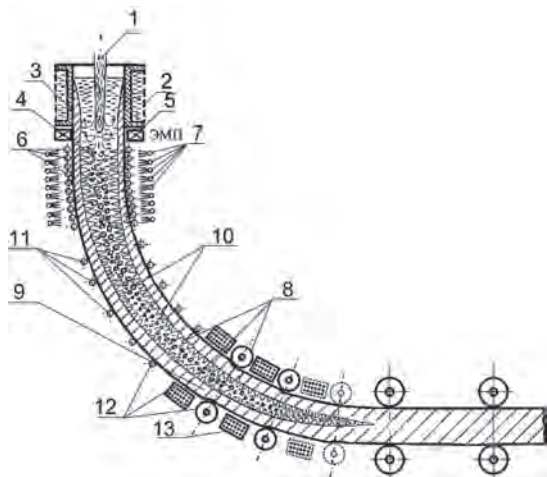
Схема МНЛЗ системой многостадийного мягкого обжатия и подогрева в зумпфовой зоне: 1 – расплав; 2 – рубашка охлаждения кристаллизатора; 3 – затвердевшая корочка; 4 – жидкая сердцевина заготовки; 5 – катушки электромагнитного перемешивания; 6 – первая секция опорных роликов; 7 – водяные форсунки зоны вторичного охлаждения; 8 – дендриты; 9 – зона деформации; 10 – скопления ликватов и неметаллических включений в жидком ядре; 11 – опорные ролики разливочной дуги; 12 – тянущее-деформирующая роликсовая клетка; 13 – индукционный нагреватель
